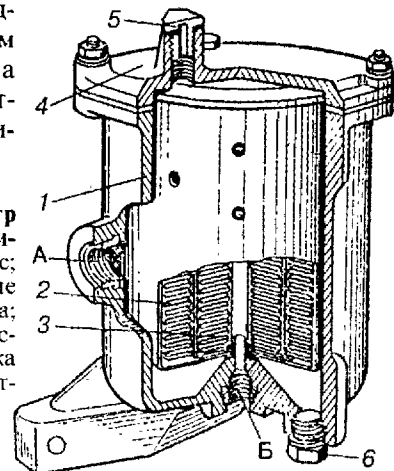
Фильтр тонкой очистки топлива (Д-245): 1 – корпус; 2 и 3 – фильтрующие элементы; 4 – крышка; 5 – вентиль для выпуска воздуха; 6 – пробка отверстия для слива отстоя
